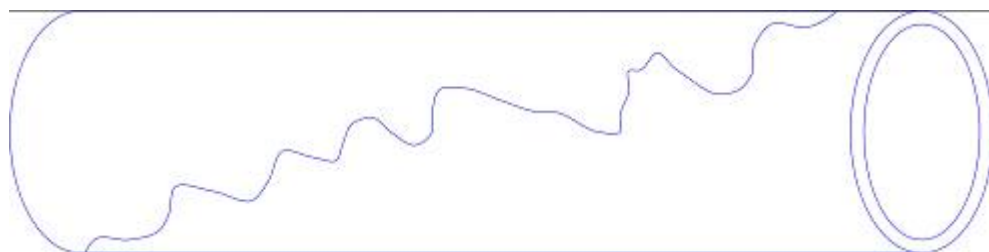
Сталеплавильная единичная плена на наружной поверхности, образующаяся при раскатывании скоплений грубых экзогенных включений на поверхности слитка и заготовки (см. рисунок А.4, приложение А)
